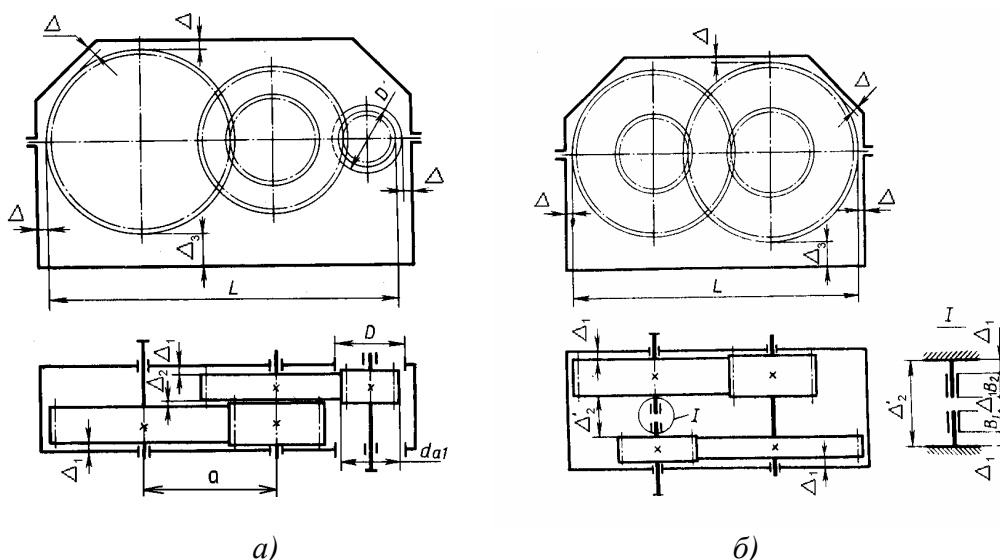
Конструктивные размеры при компоновке цилиндрических редукторов
